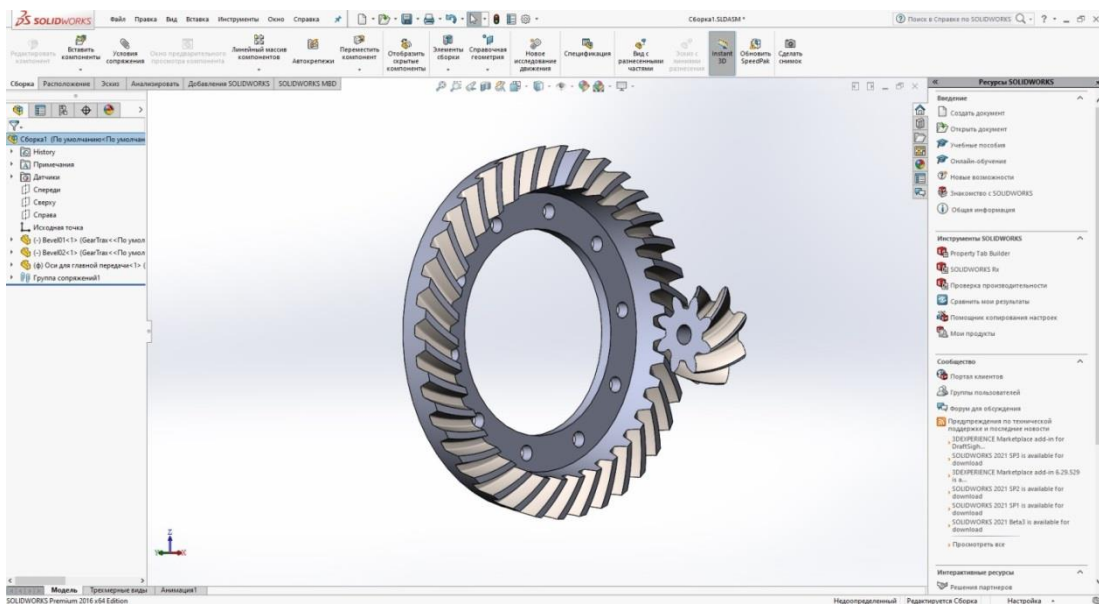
3D модель зубчатого зацепления передачи
